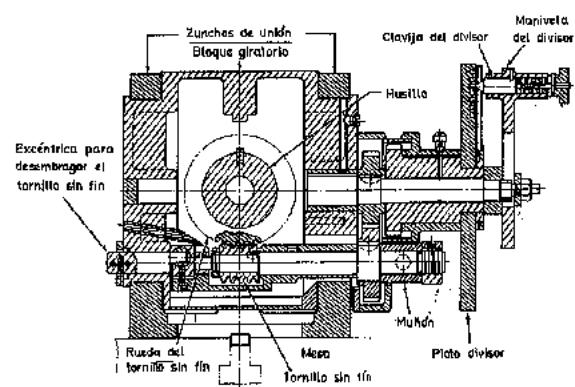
Sección longitudinal de un cabezal divisor mostrando el tornillo sin fin, la rueda helicoidal y el eje del tornillo (Cincinnati Milling Machine Co.)
